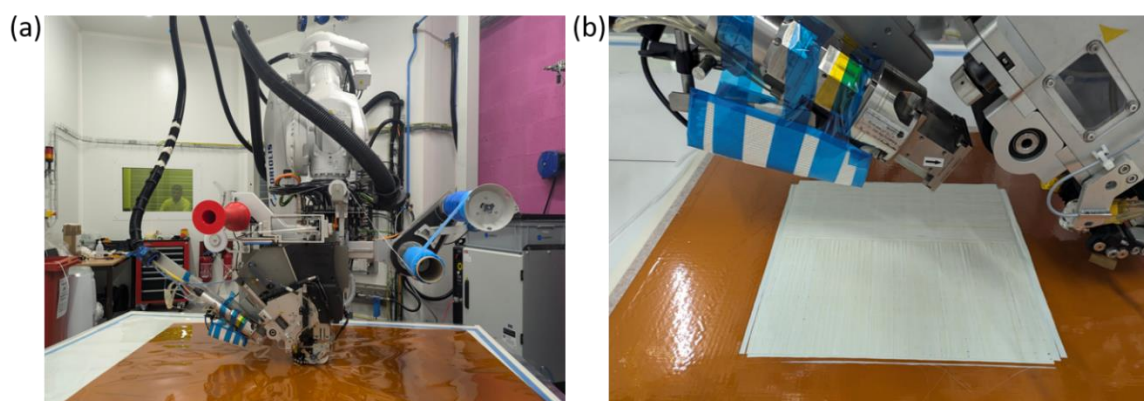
(a) Machine de dépose AFP C-Solo (Compositadour, Bayonne) utilisée pour la fabrication et (b) Photo prise pendant la fabrication de la plaque 8 plis $[0/90/0/90]_s$ de $260 \times 260 \text{ mm}^2$ à partir d'une bobine de mèche imprégnée de composition B5G20.
